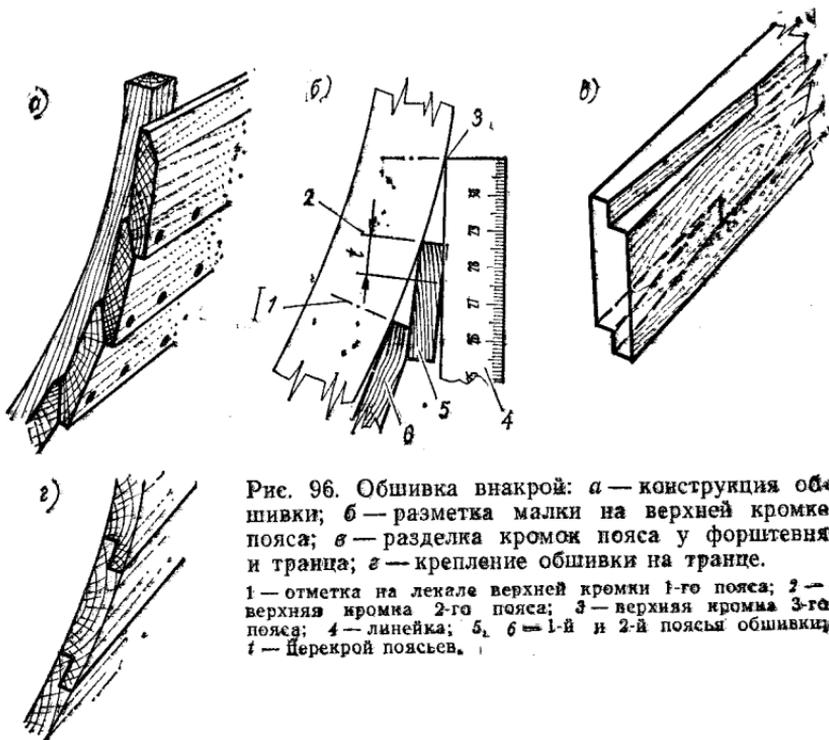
Обшивка внакрой: а — конструкция обшивки; б — разметка малки на верхней кромке пояса; в — разделка кромок пояса у форштевня и транца; г — крепление обшивки на транце.
